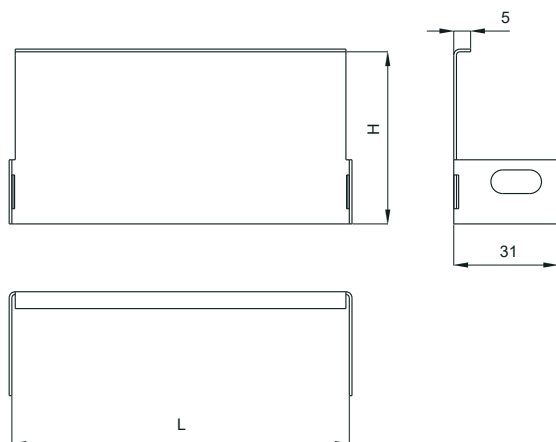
Заглушка / Figure B.1 – Ending flange
